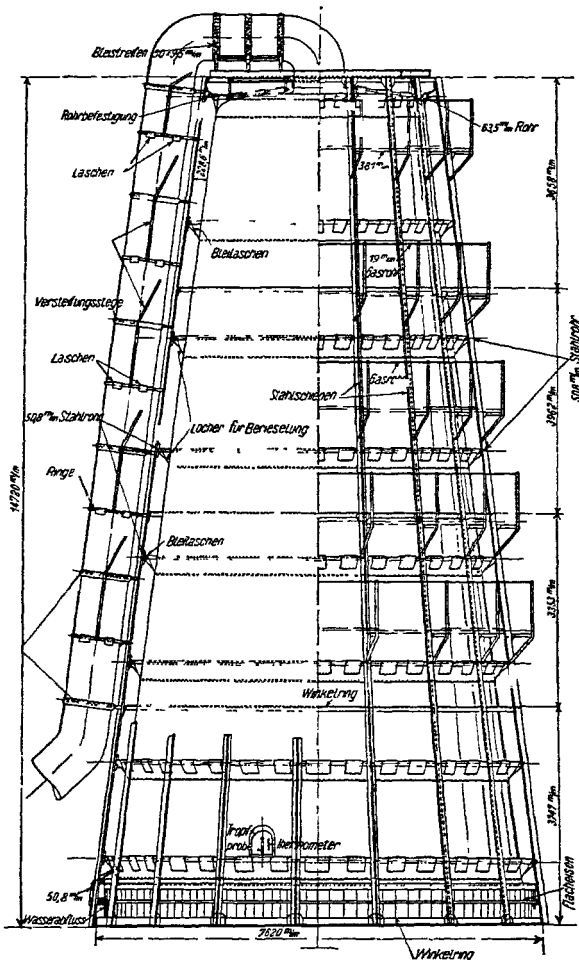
MILLS-PACKARD-Kammer aus WAESER.
